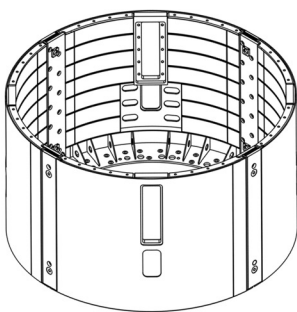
Корпус стабилизирующей секции опытного образца геохода
